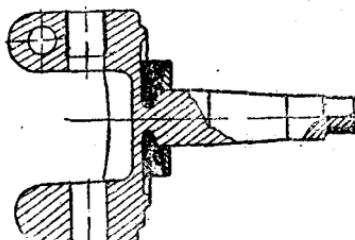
堆焊后变成原来油封座圈的尺寸
